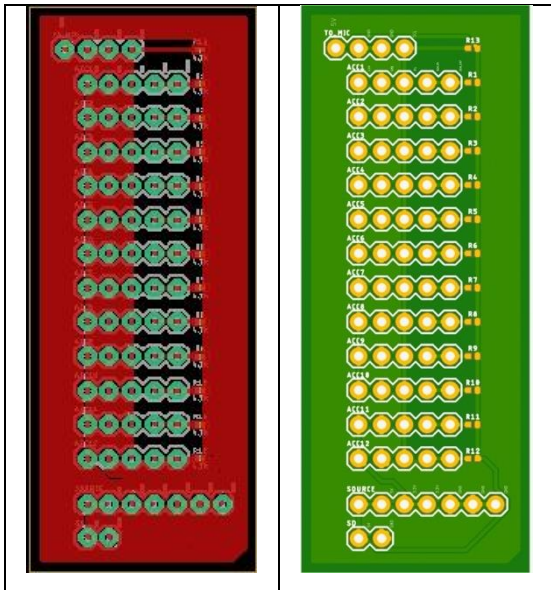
PCB diseñada, A) Versión digitalizada, B) Versión pre-impresión.
